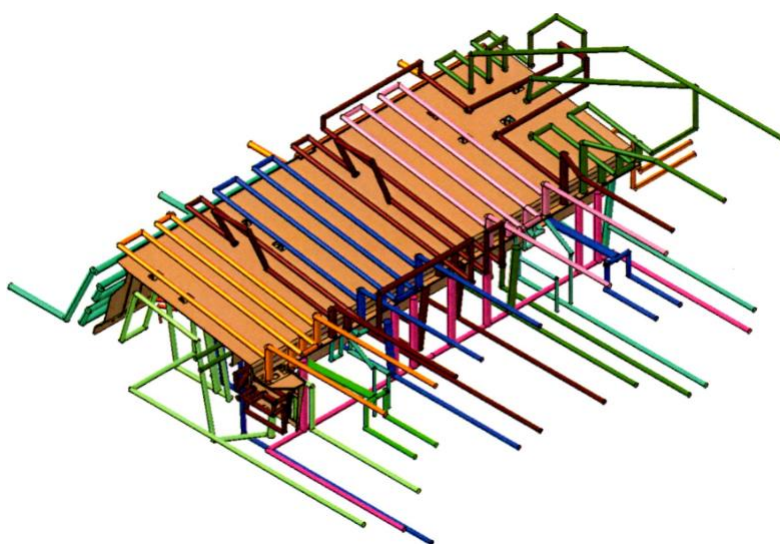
Vista isométrica de toda a refrigeração do molde.
